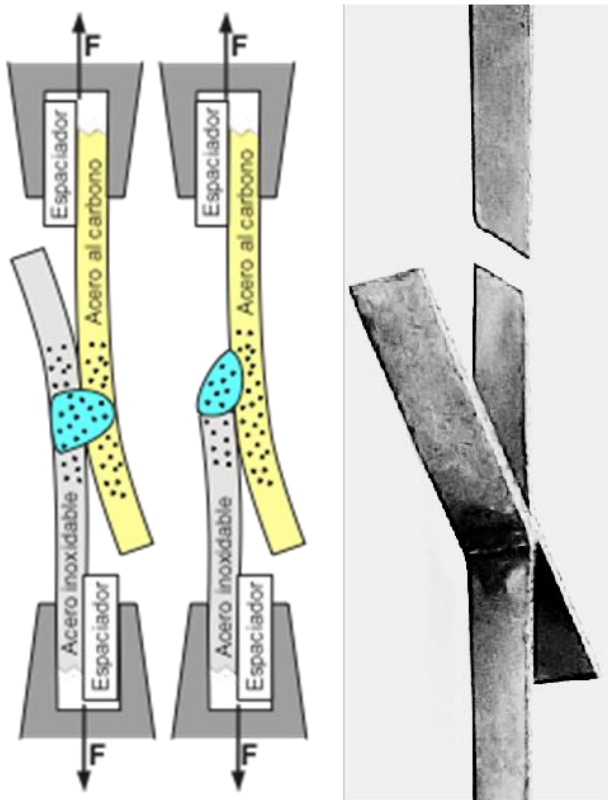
Dispositivo del ensayo de tracción de probetas con uniones soldadas láser a tope y en esquina, e imagen final de una de ellas.
